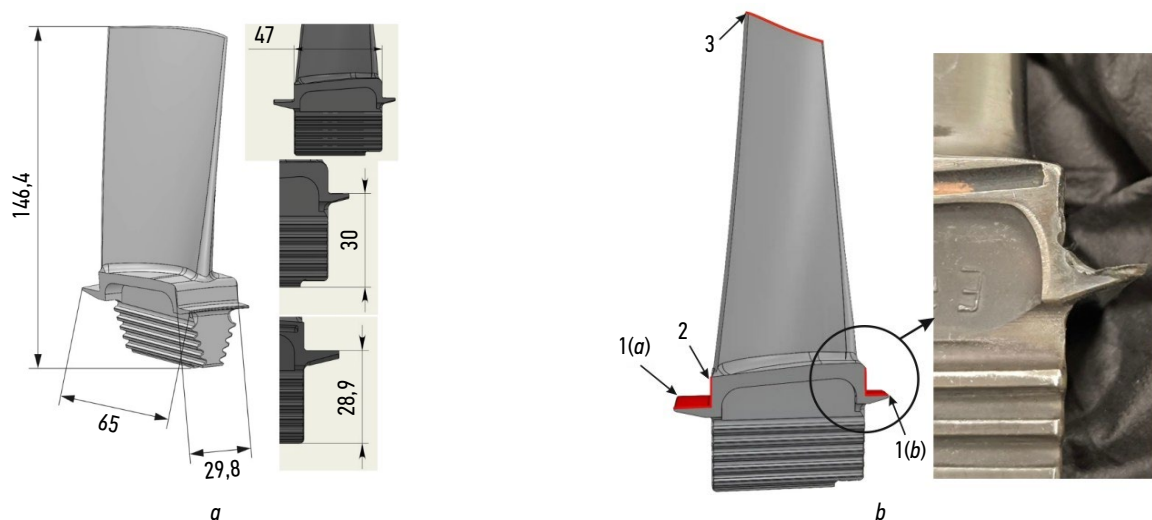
Внешний вид рабочей лопатки ДР-59Л: *a* — размеры рабочей лопатки; *b* — изношенные поверхности рабочей лопатки.
